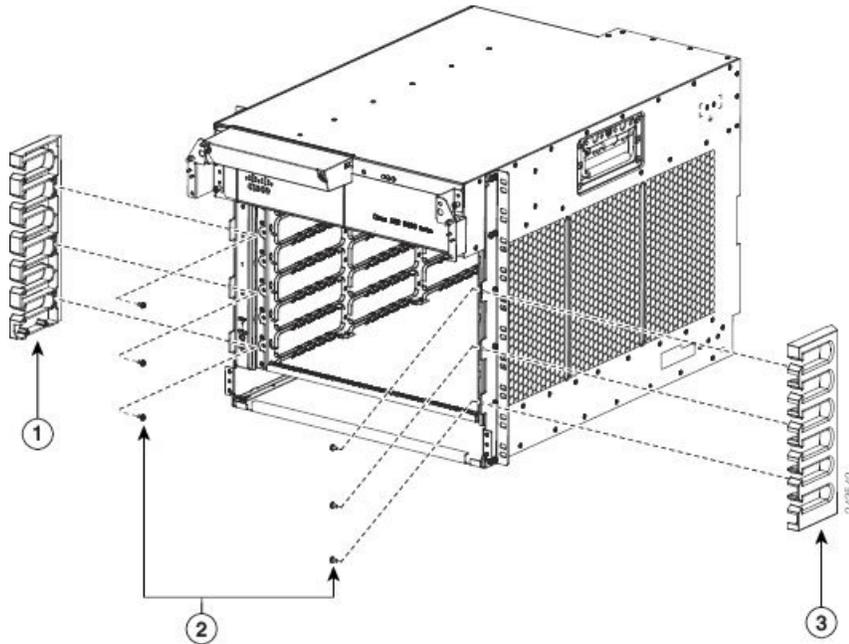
Instalación del accesorio para la puerta de la bandeja del ventilador de plástico y los soportes de montaje metálicos en el router Cisco ASR 9006
